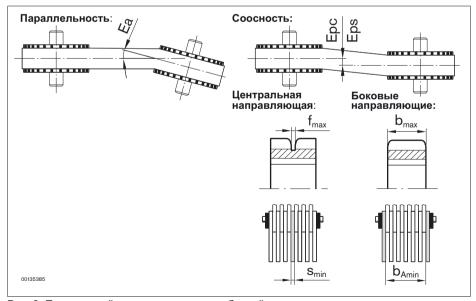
Правильный монтаж звездочек зубчатой цепи
